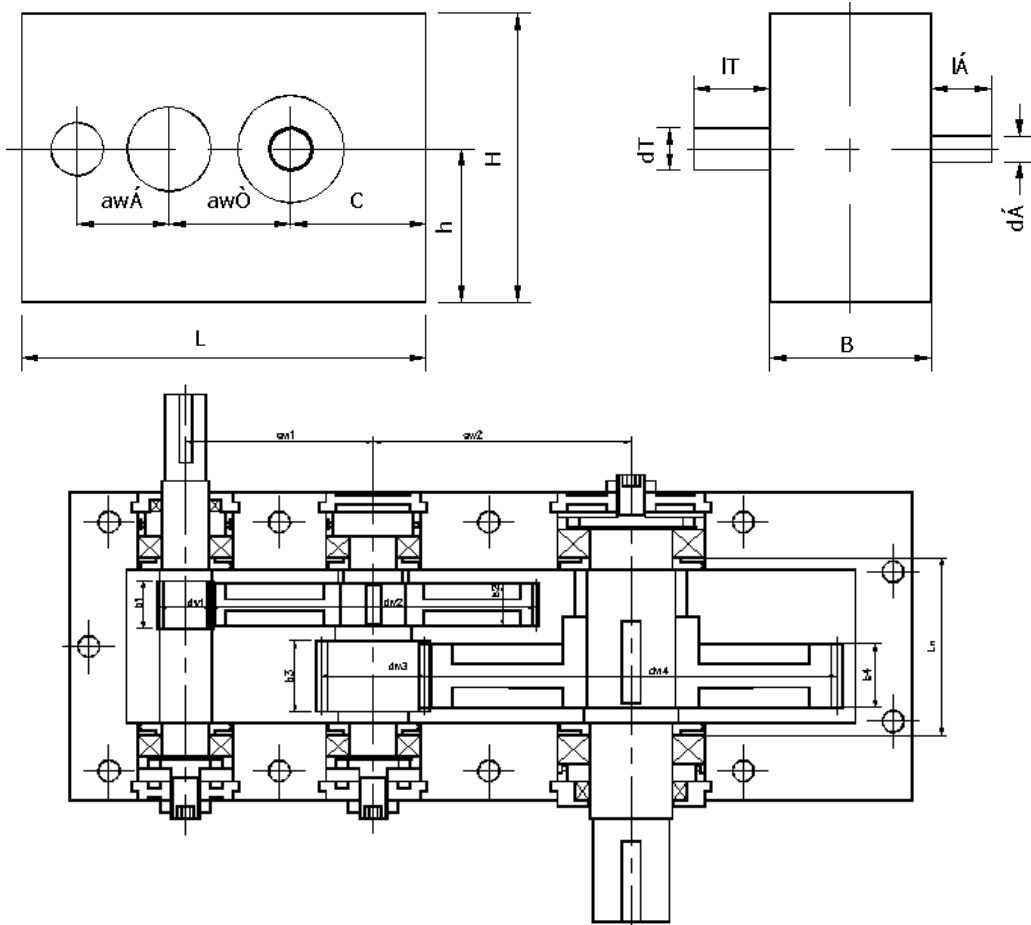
Габаритный чертёж и компоновка передач двухступенчатого цилиндрического редуктора типа Ц2У по ГОСТ 20758-75.
